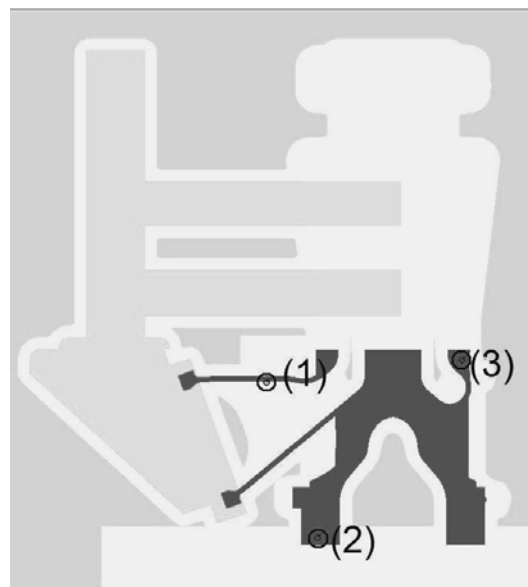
Схема расположения виртуальных термопар на сечении отливки «корпус»:
